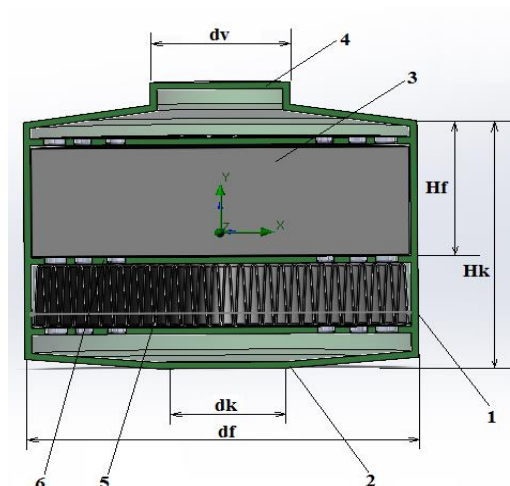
Вид конструкції фільтрувальної коробки з газовим фільтром: 1 - корпус фільтра; 2 - кришка коробки з входним отвором; 3 - газовий фільтр; 4 - отвір клапана вдиху; 5 - протипиловий фільтр; 6 - решітка
